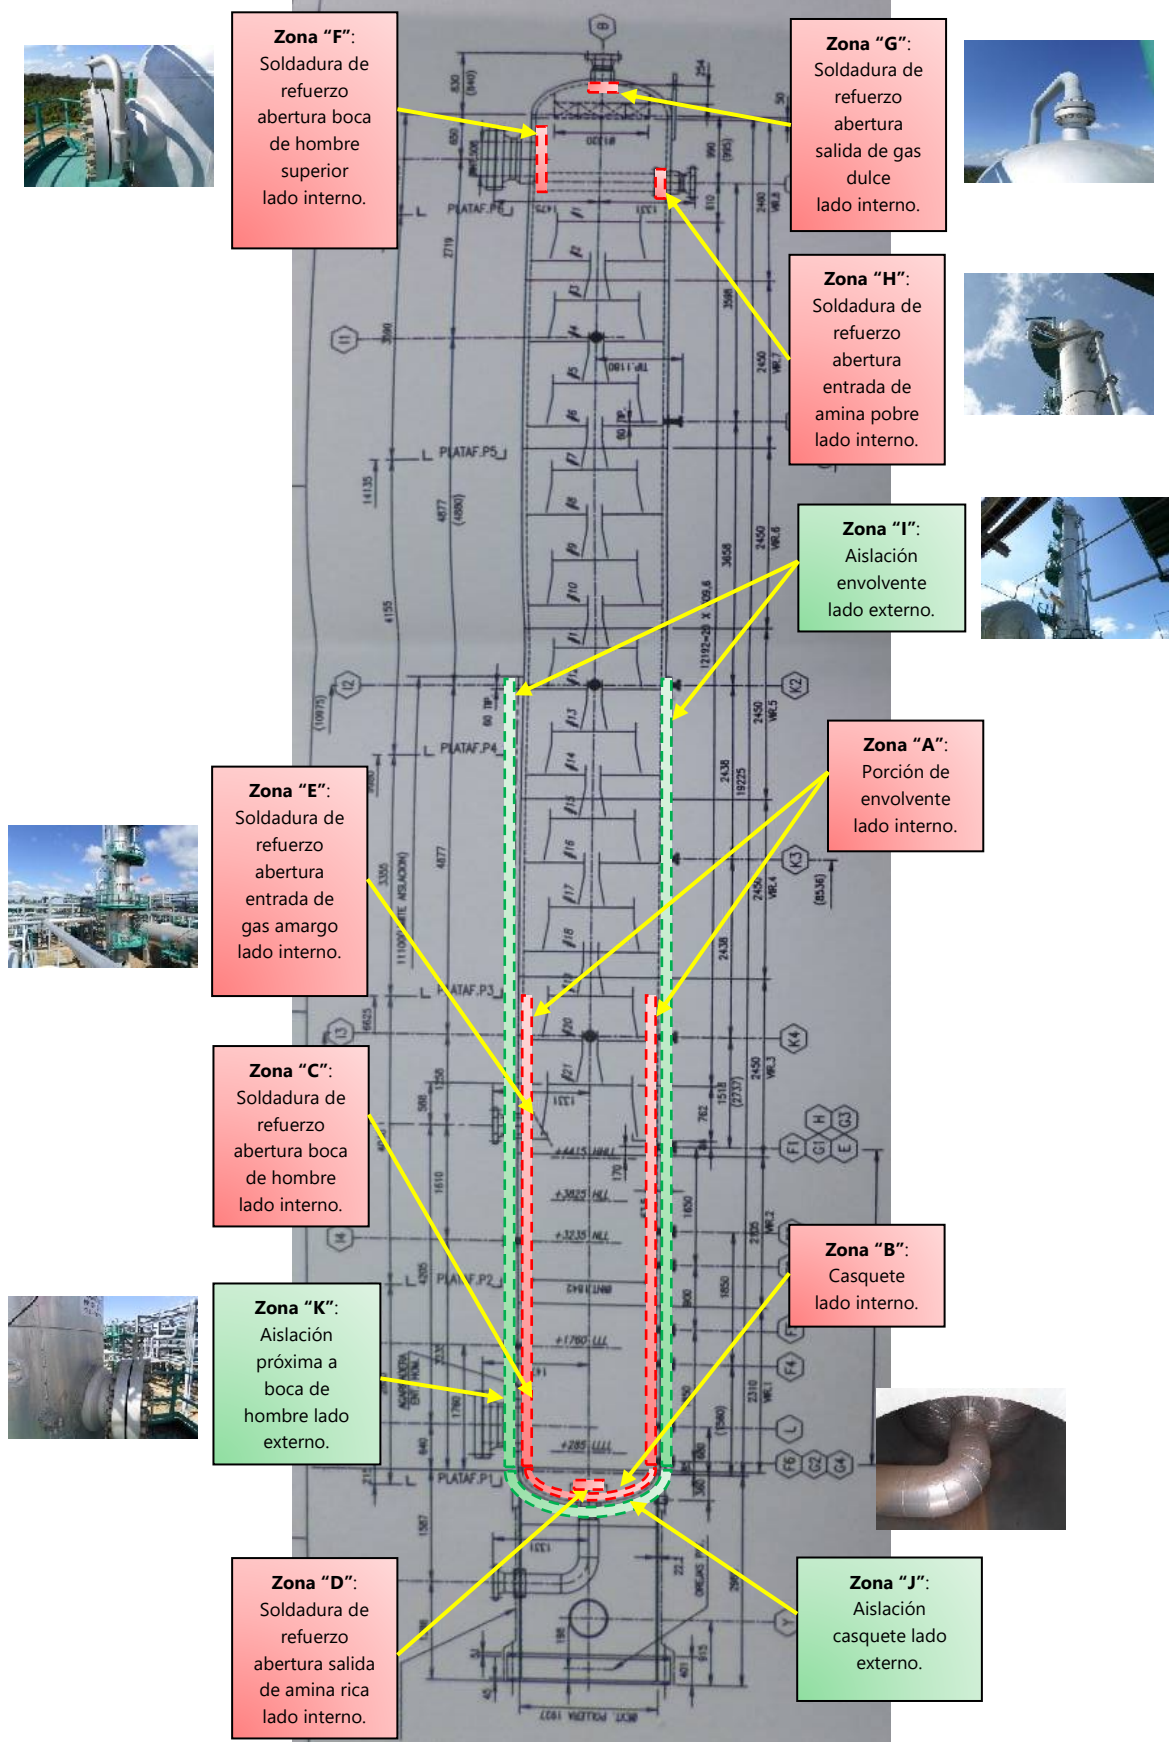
Fragmento del plano constructivo de la torre contactora en corte enviado por el fabricante.
